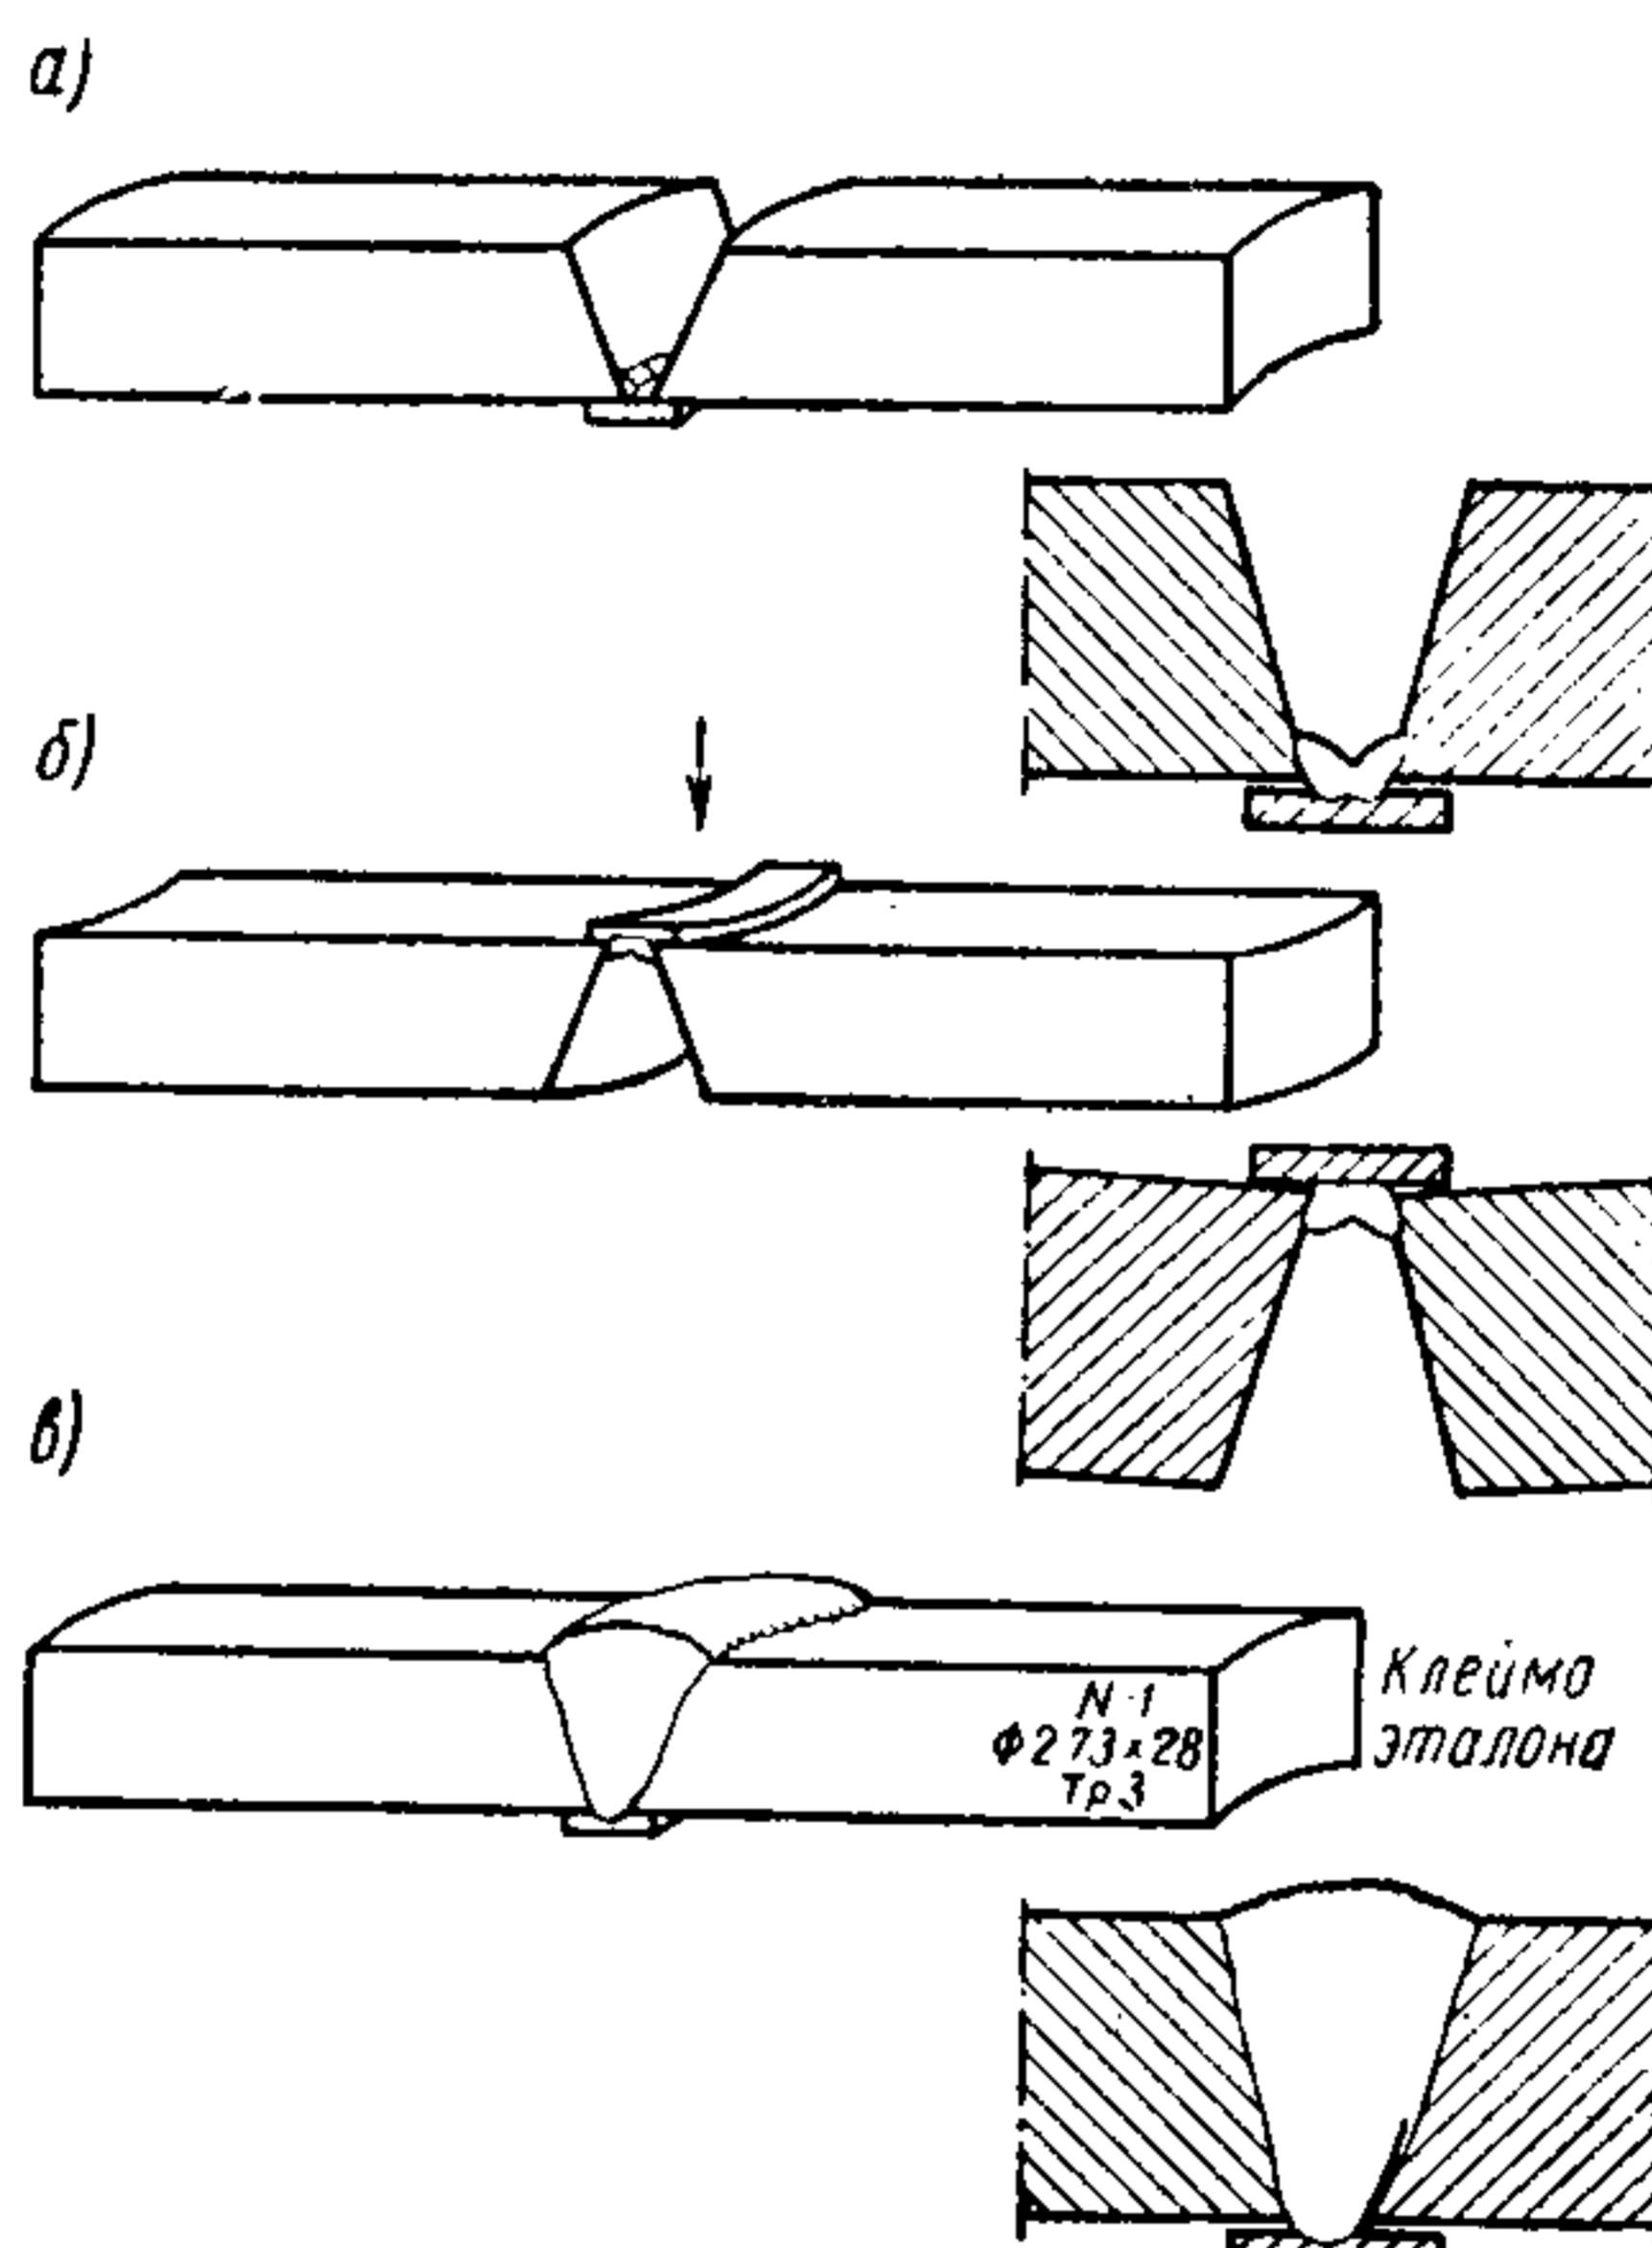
Изготовление эталонного образца с трещиной в корне шва
